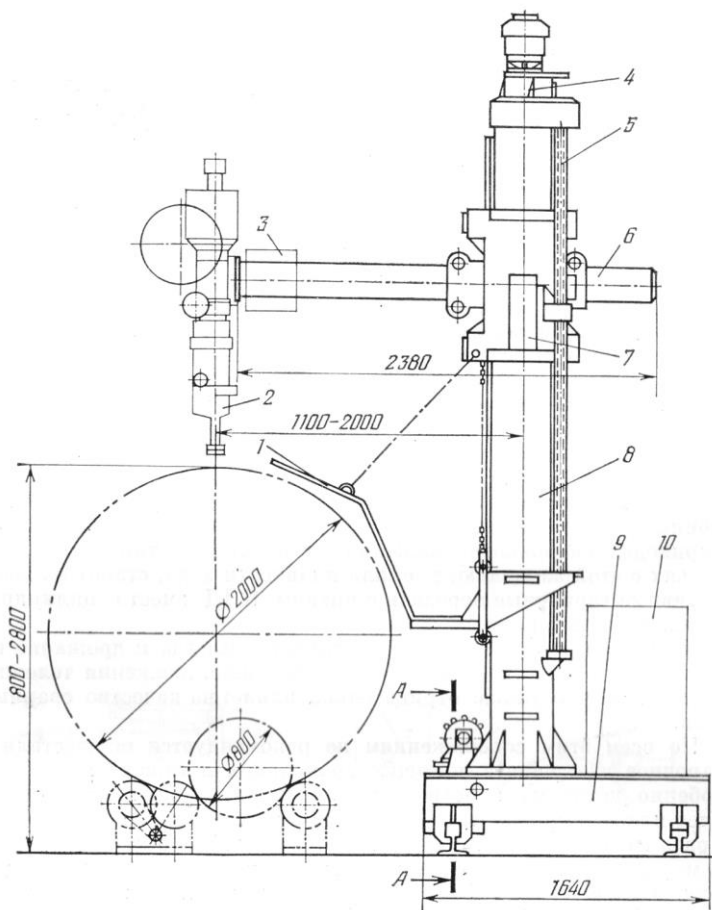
Глагольная тележка ГТ-1: 1 – щиток-подлокотник; 2 – сварочная головка; 3 – пульт управления; 4 – механизм подъема каретки; 5 – подъемный винт; 6 – выдвижная штанга; 7 – каретка; 8 – колонна; 9 – тележка; 10 – шкаф аппаратуры управления
